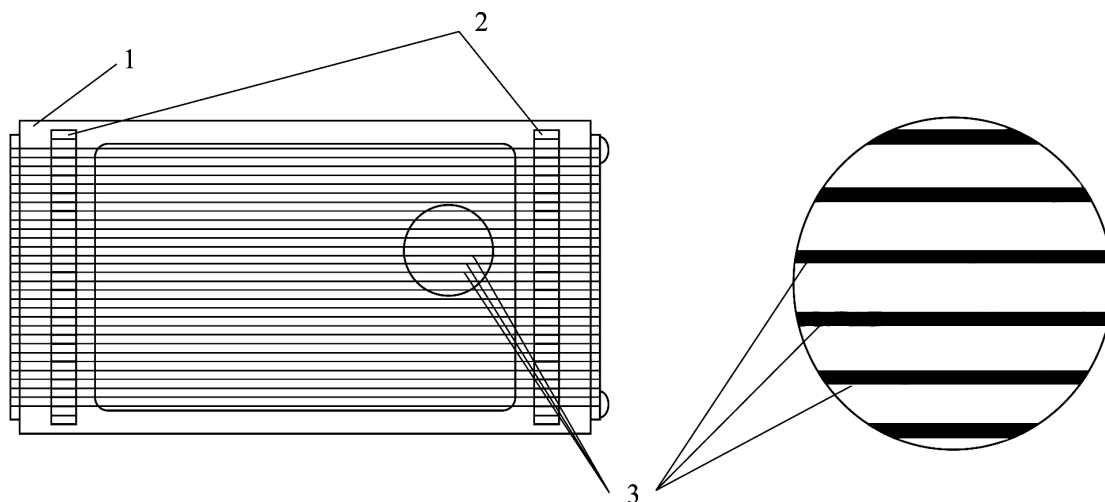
Інструмент для різання струнами з використанням вільного абразиву. 1 – інструмент; 2 – розмірні планки; 3 – струни.
